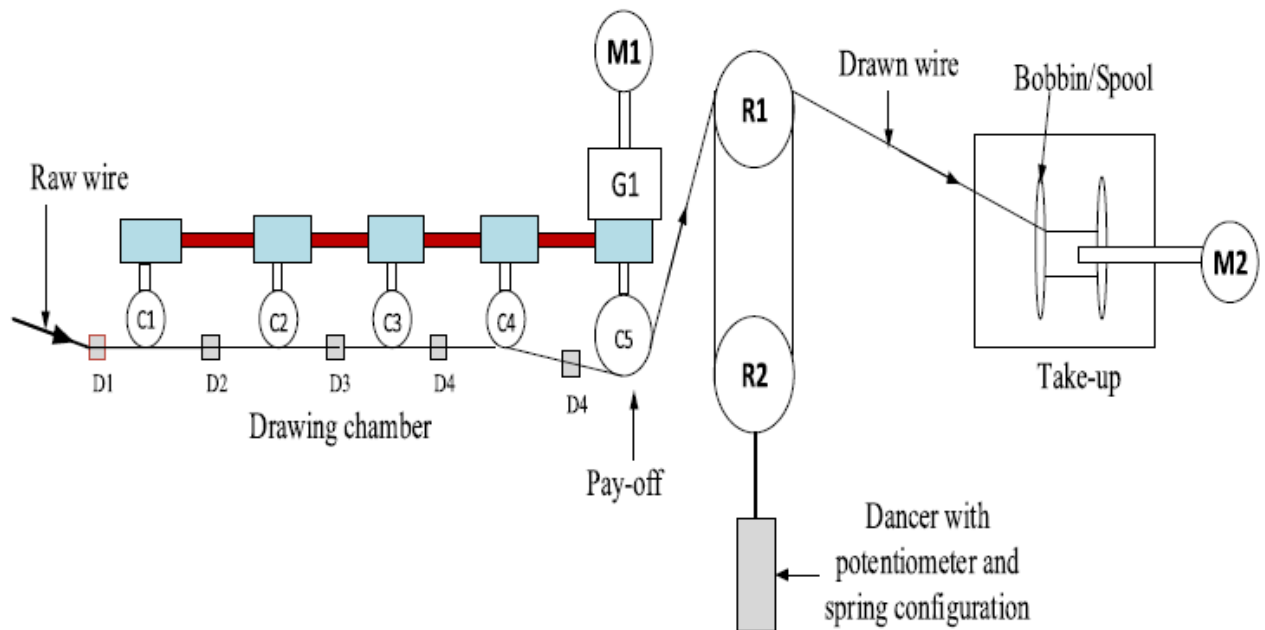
Принципова схема процесу волочіння дроту з механізмом витягування, натягу та диска намотування: M1 - двигун витягування; M2 - двигун прийому; C1-C5 - шпильки; G1 - коробка передач; D1-D5 - волочильні штампи; R1, R2 – валки «дансера».
